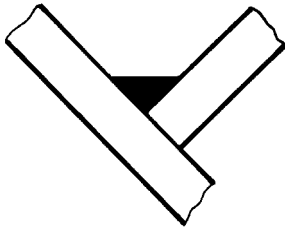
Downhand fillet weld / Liggande källsvets
